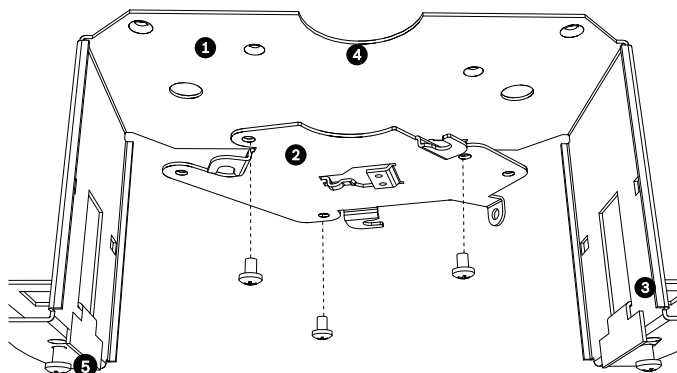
Fixar a placa de montagem ao suporte de montagem
